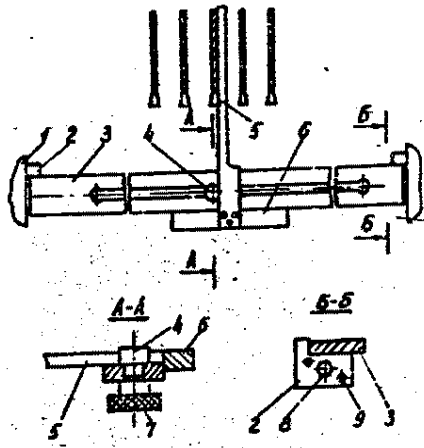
Линейка и угольник для выверки положения пил в пильной рамке: 1 - станина; 2 - планка; 3 - линейка; 4 - гайка – упор; 5 - стержень угольника; 6 - пластина угольника; 7,8-болты; 9 - штифт.
